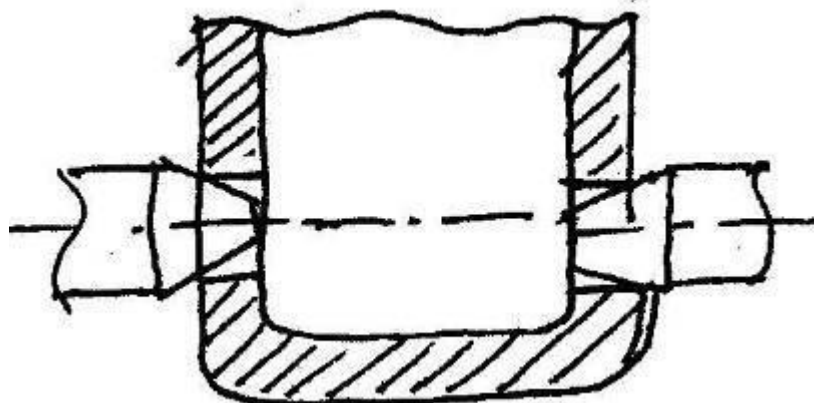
Схема базирования корпуса по коническим оправкам
